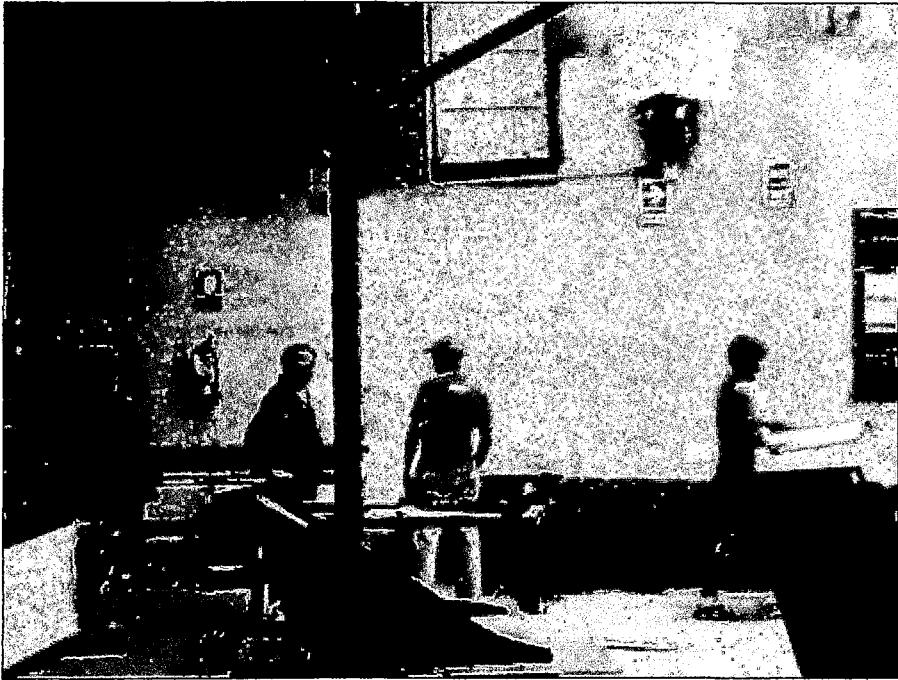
TRABAJADORES SIN EQUIPOS DE
